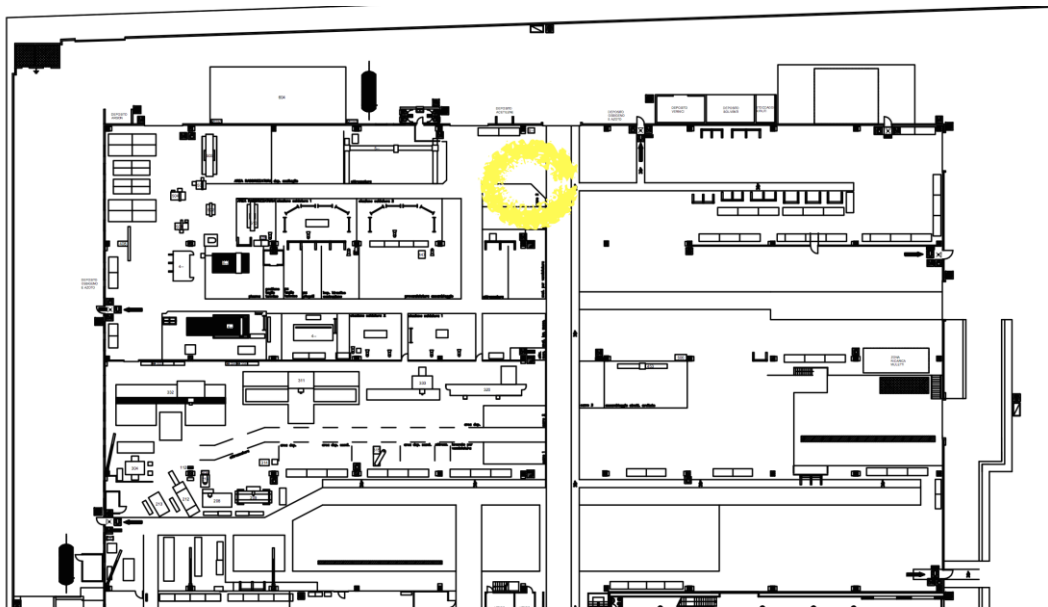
10: Localizzazione sulla pianta dello stabilimento della zona di raccolta componenti
